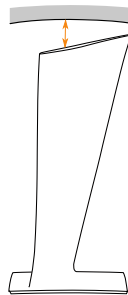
Interface aube/carter : aube de turbomachine (□), carter environnant (■) et jeux aube/carter (↔).
